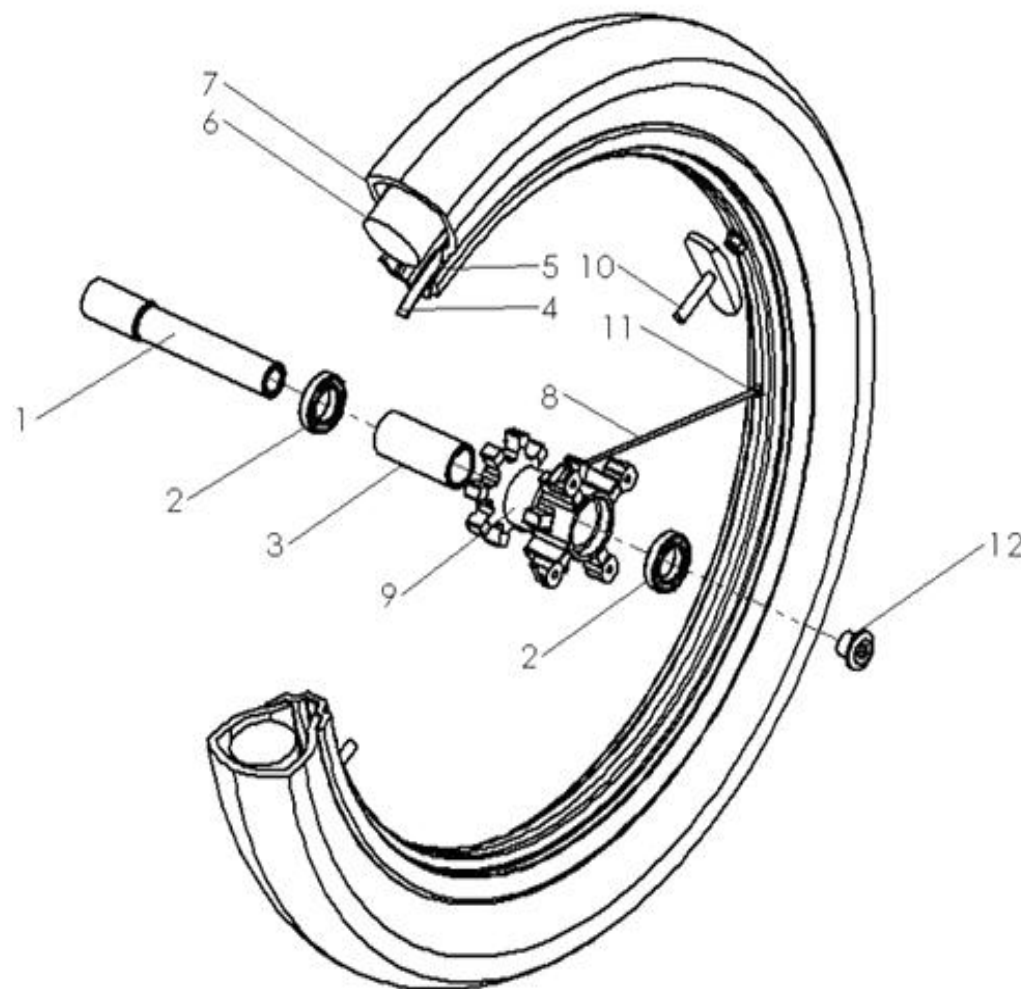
ROUE AVANT / FRONT WHEEL / RUEDA DELANTERA
